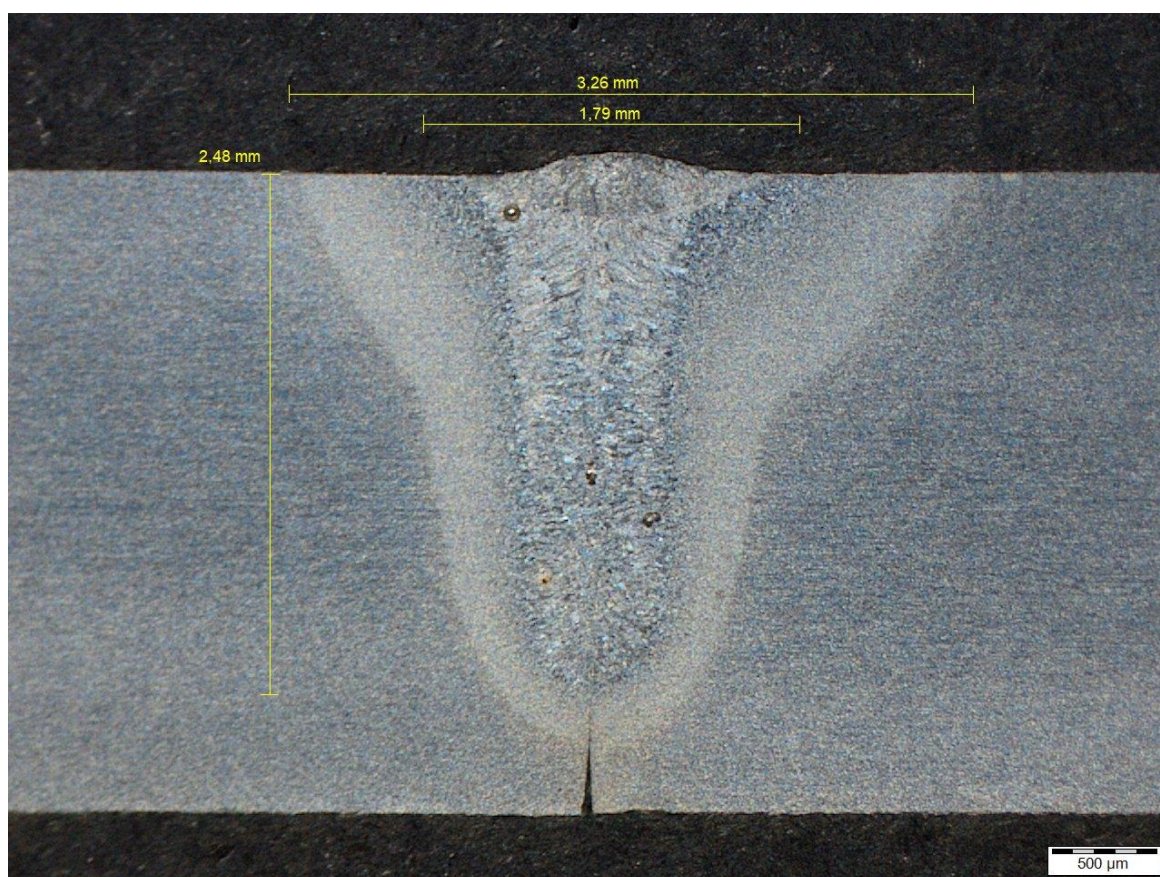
Makrostruktura svaru (laser s předehřevem TIG – vzdálenost elektrody 4 mm)
